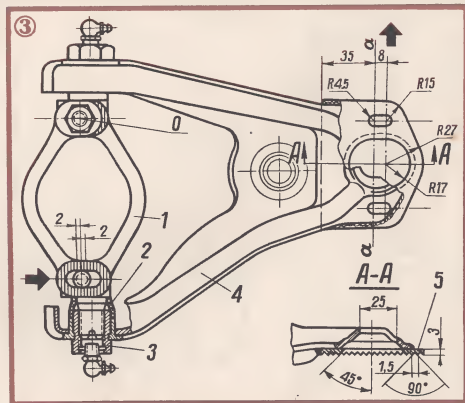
Измененный верхний рычаг: 1 — ось; 2 — резиновая втулка; 3 — резцовая втулка; 4 — собственно рычаг; 5 — зубчатая пластина рычага.
